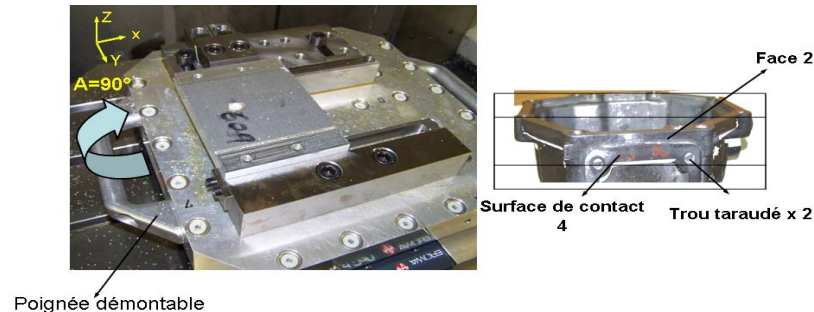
La rotation de la table de la machine pour accéder à la face 2
